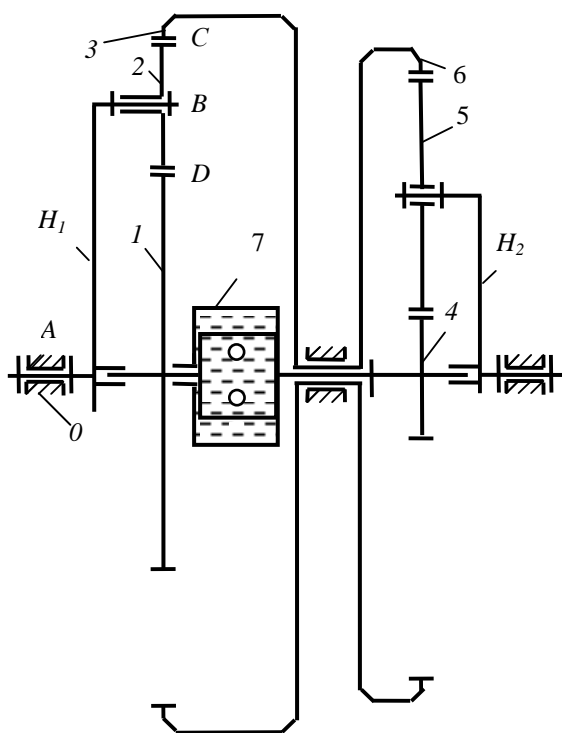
Статически определяемый зубчатый адаптивный вариатор
